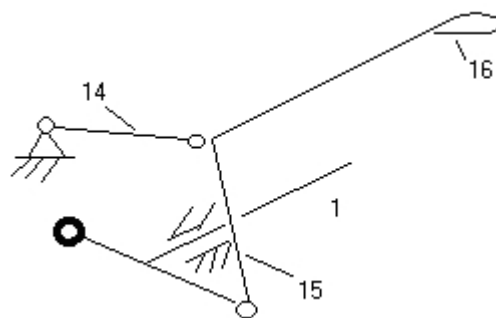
Механізм ниткопритягувача швейної машини 1022М
